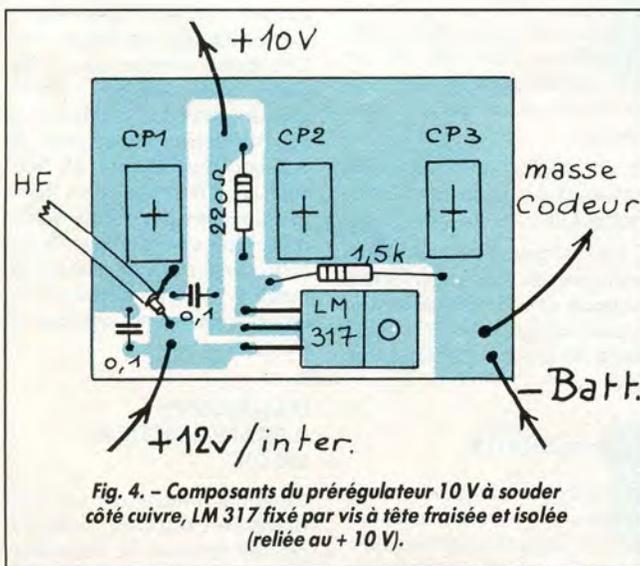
Composants du pré-régulateur 10 V à souder côté cuivre, LM 317 fixé par vis à tête fraisée et isolée (reliée au +10 V).
